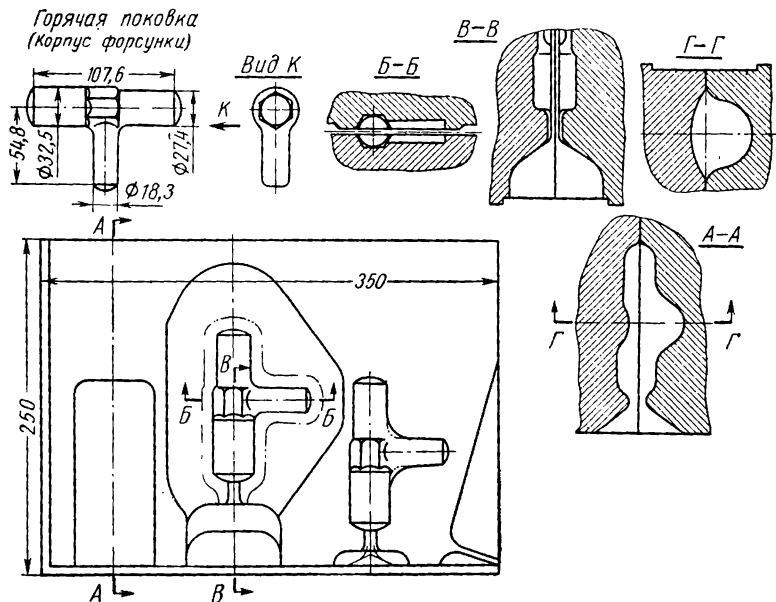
Молотовый штамп для поковки корпуса форсунки
